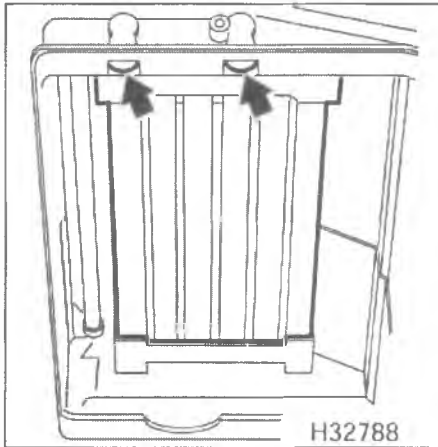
Высвободите выступы шпилек крепления нагревательного элемента РТС из их установочных отверстий в кожухе отопителя (отмечены стрелками)
